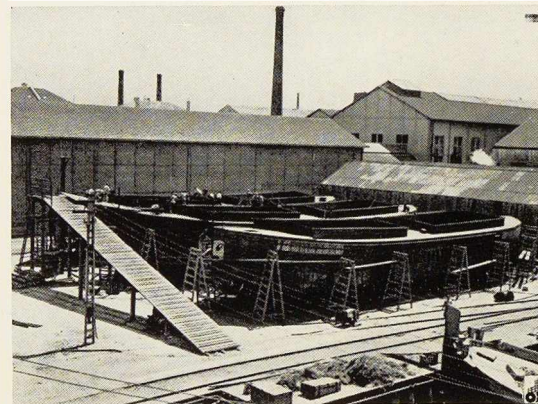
Série de 3 allèges en cours de construction aux Ateliers C. U. F. à Barreiro.
